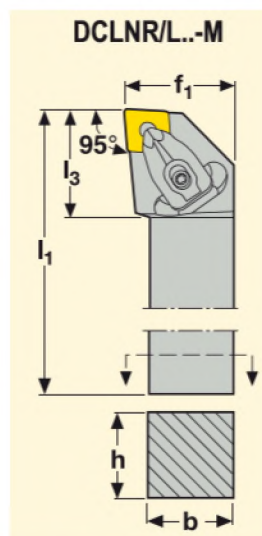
Державка DCLNR2525M12-M [6, с.82]
